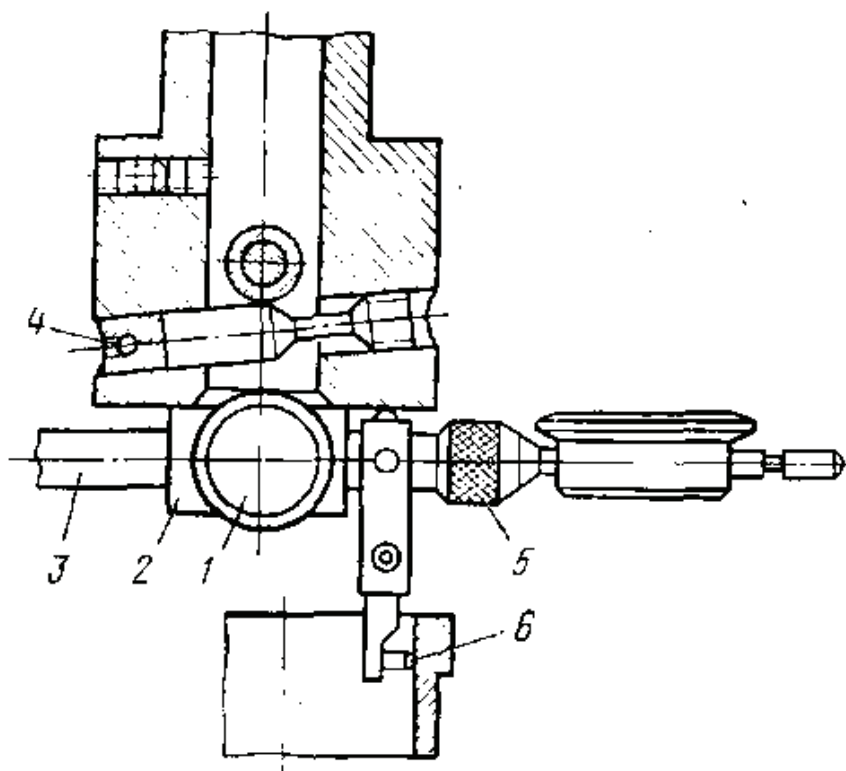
Резцовая головка с приспособлениями для центрирования гильз:
